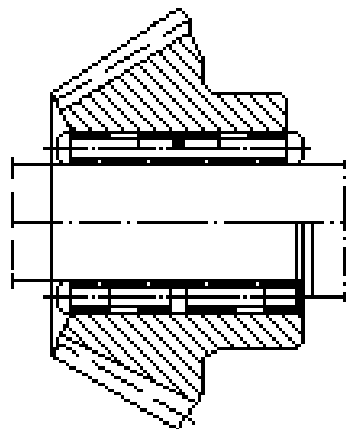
Fixação de engrenagem cônica com bucha HBK
